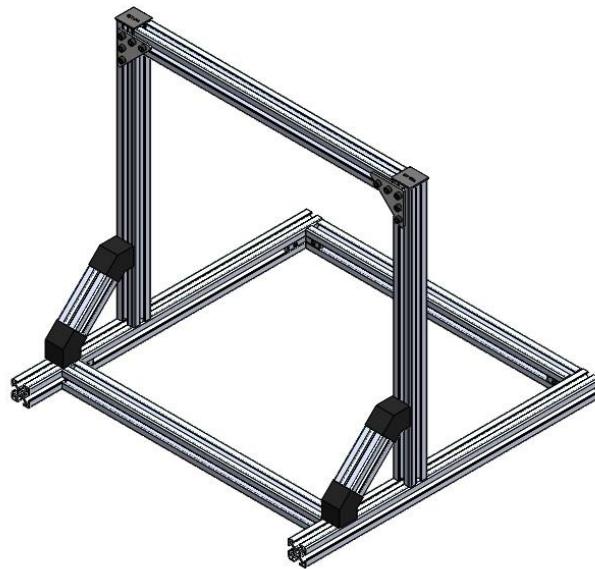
Ensamblaje estructura; Fuente: Elaboración propia con SW
